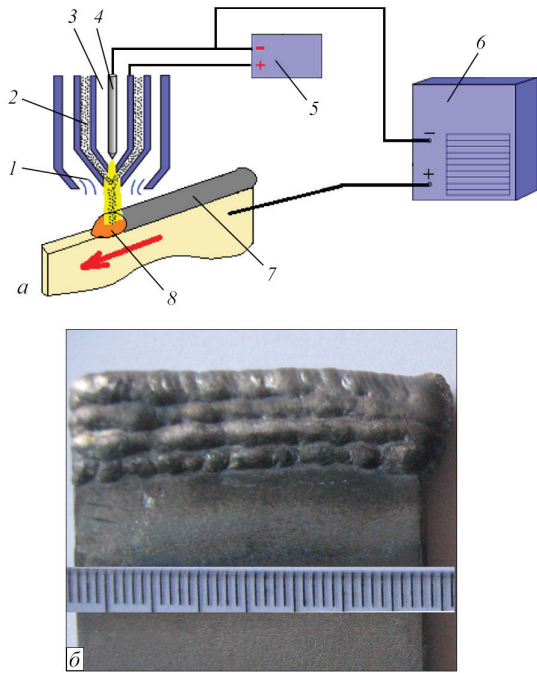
Схема микроплазменной порошковой наплавки на узкую подложку (а) и внешний вид соответствующей технологической пробы при многослойной наплавке (б) (1 — защитный газ; 2 — транспортирующий газ и порошок; 3 — плазмообразующий газ; 4 — W-электрод; 5 — источник питания дежурной дуги; 6 — источник питания микроплазменной дуги; 7 — наплавленный валик; 8 — сварочная ванна
